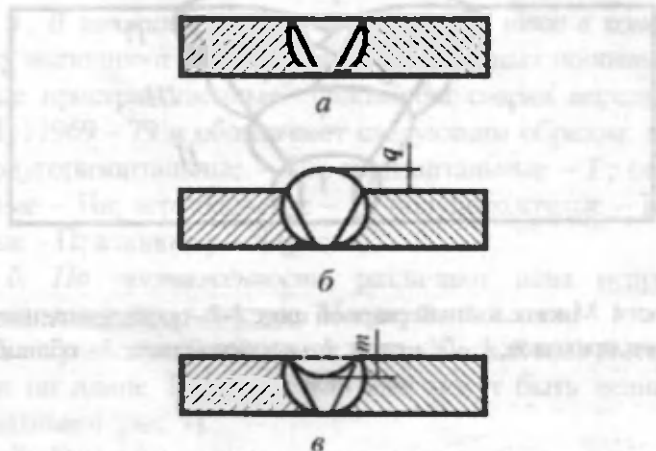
Сварные швы: а – нормальные; б – выпуклые; в – вогнутые
